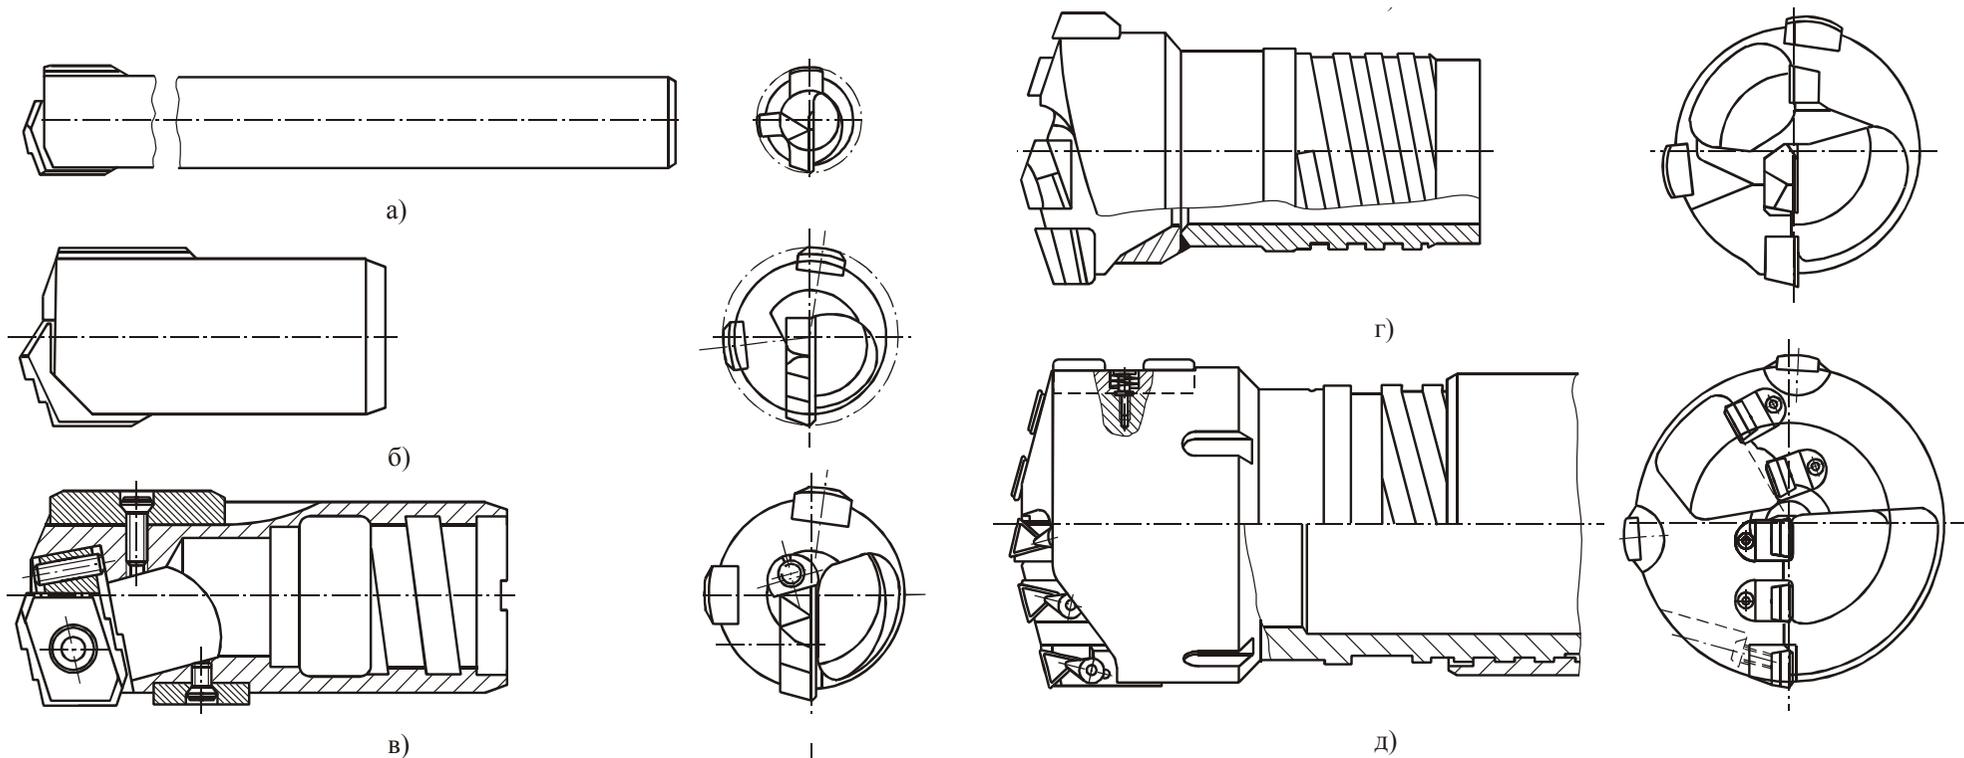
Сверлильные головки БТА: *a* – однокромочное сверло с напайной Т-образной твердосплавной пластиной ($d = 6...18$ мм);
